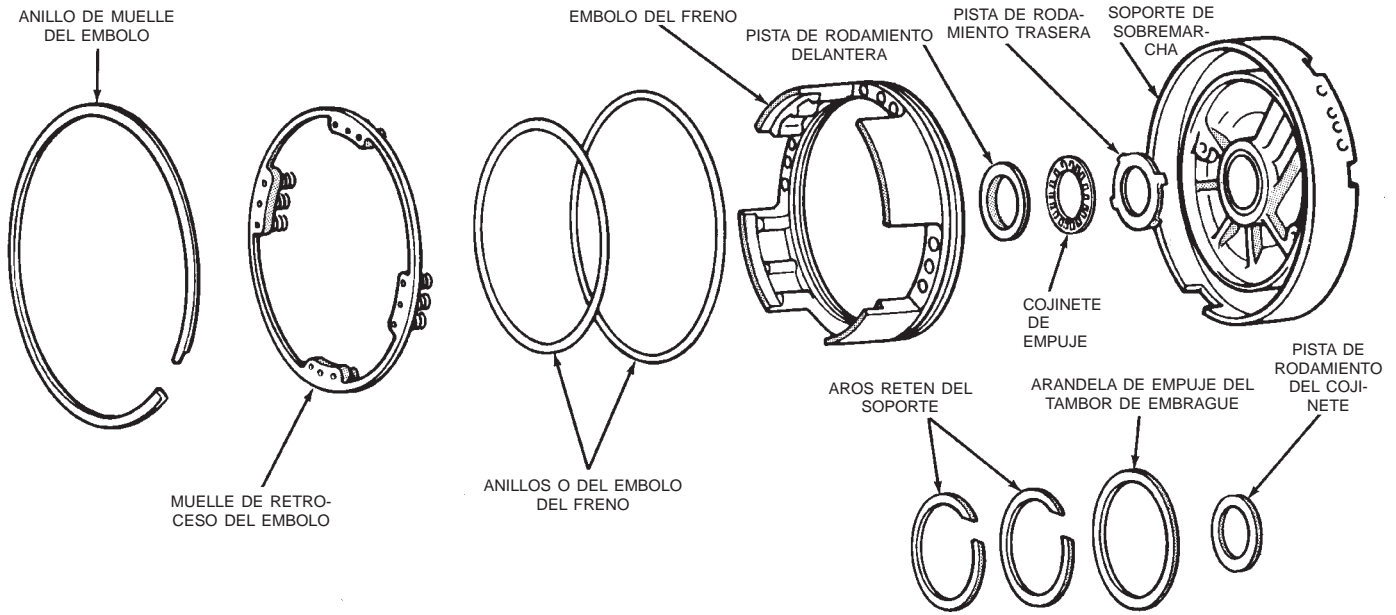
Desmontaje e instalación del anillo de muelle del émbolo
